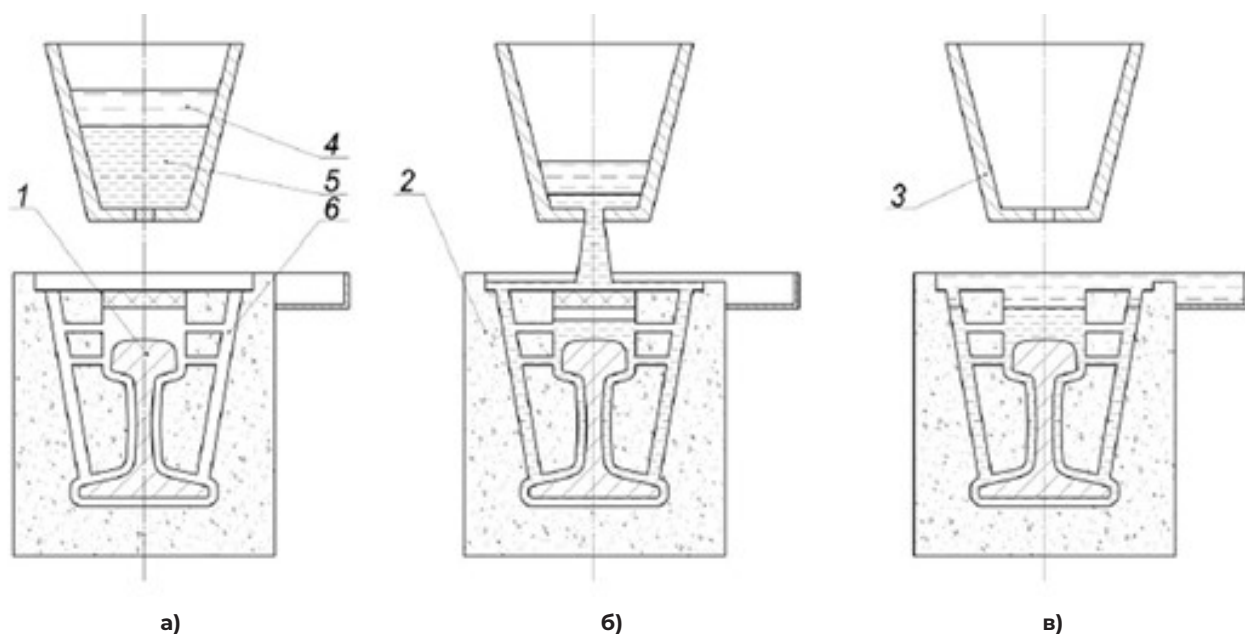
Схема термитной сварки рельсов: а – плавление термитной смеси; б – заливка расплавленной термитной смеси в форму; в – кристаллизация сварного шва; 1 – рельс, 2 – форма, 3 – тигель, 4 – расплавленный шлак, 5 – расплавленный металл, 6 – литник.
